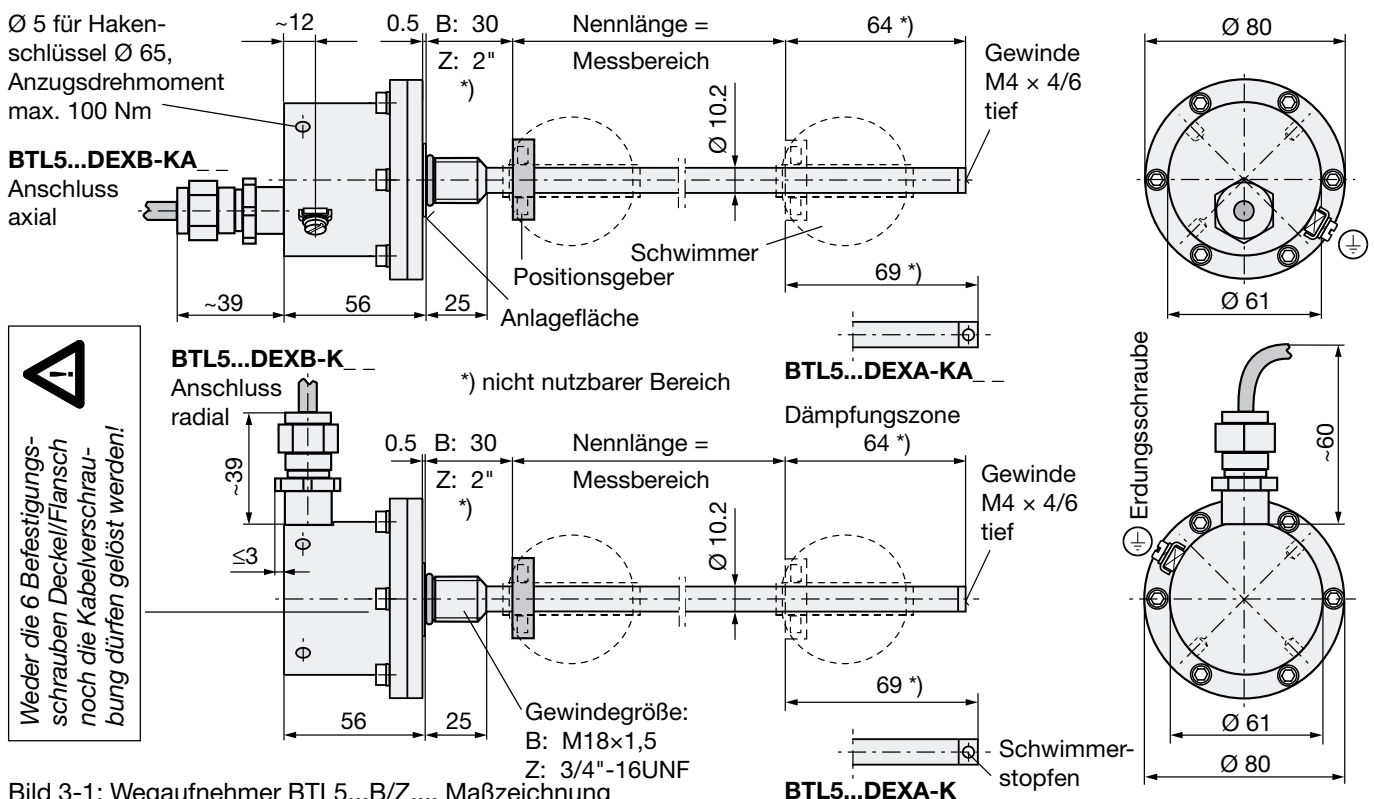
Wegaufnehmer BTL5...B/Z..., Maßzeichnung
